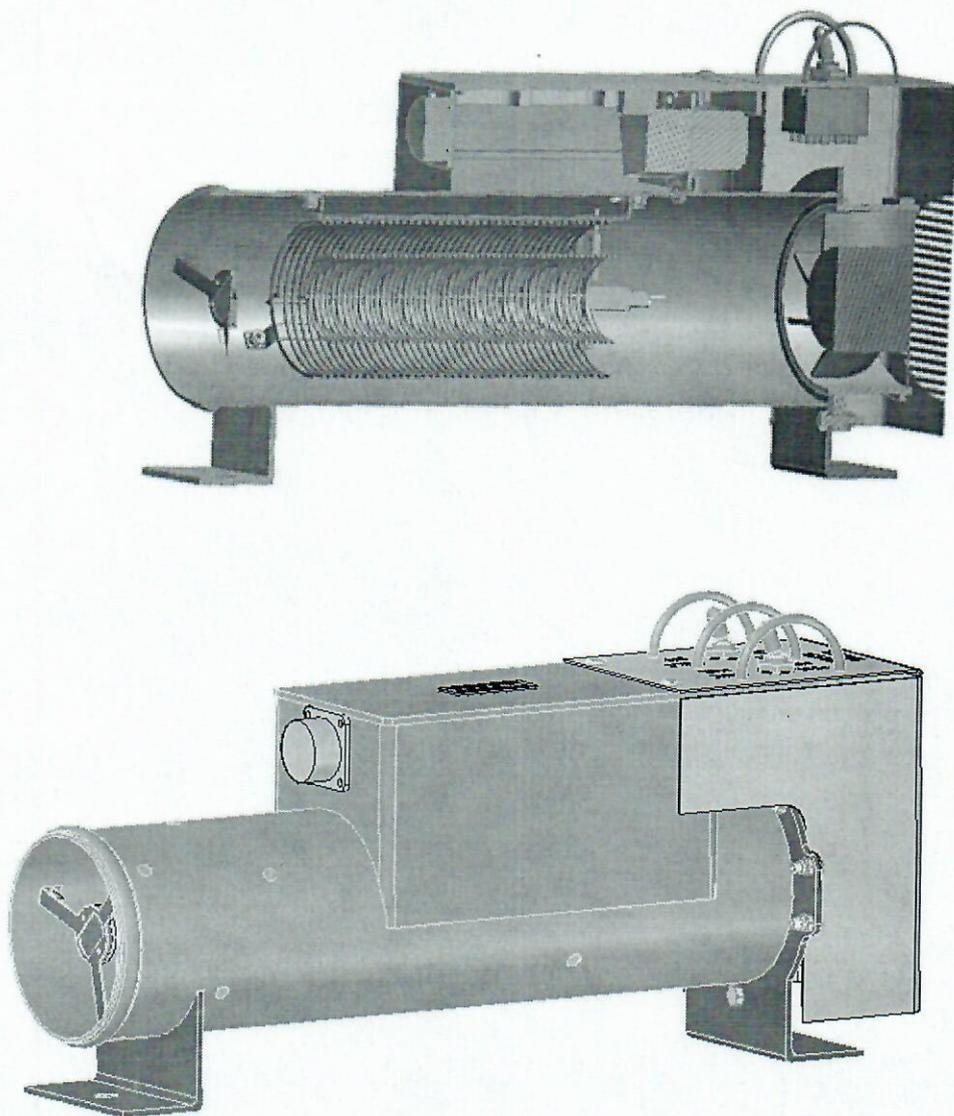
внешний вид агрегата обогрева транспортной кабины
